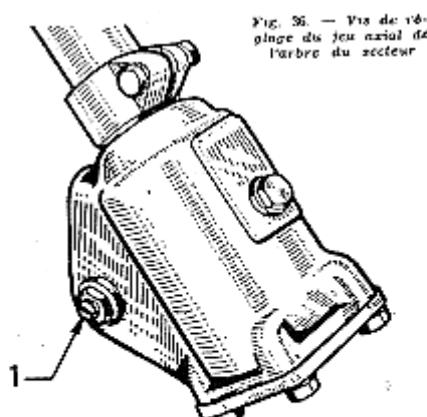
Vis de réglage du jeu axial de l'arbre du secteur
